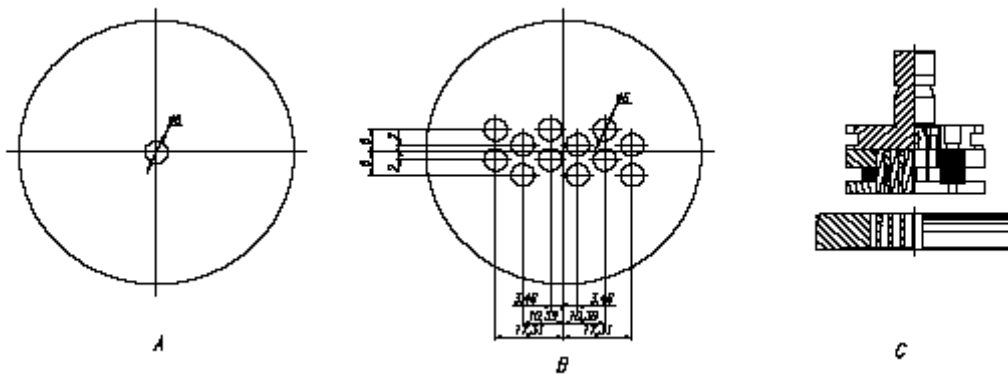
a- Punção único; b- geometria com doze punções; c- Ferramenta montada
